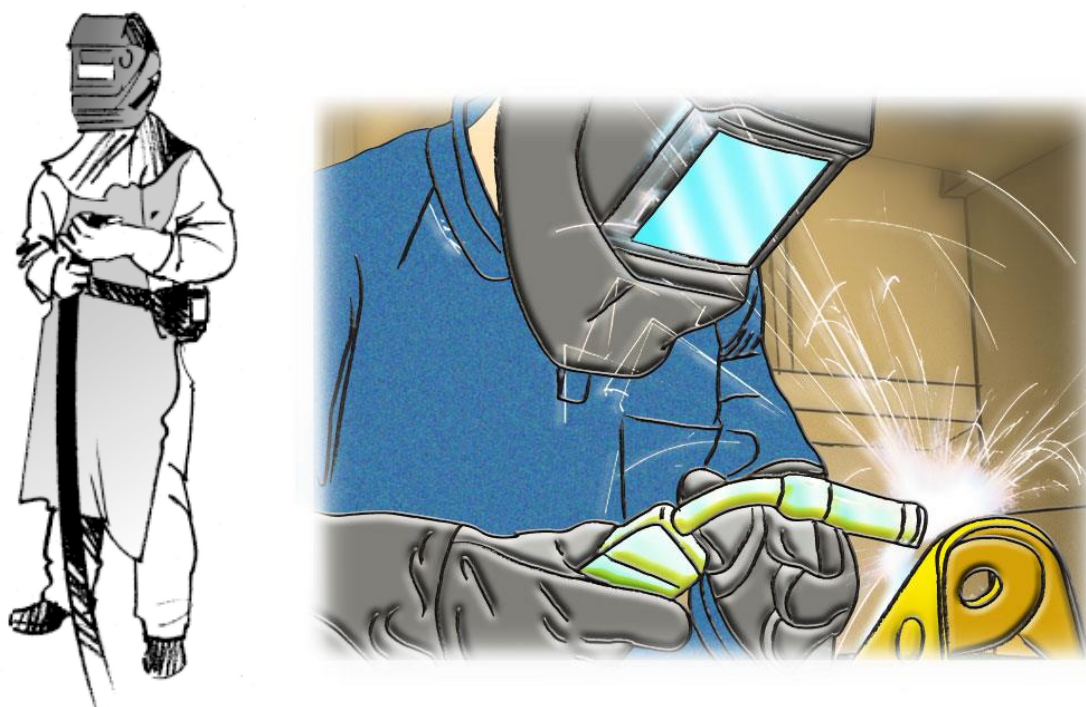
EPI's essenciais para o soldador (esquerda) e detalhe da máscara de soldagem (direita).
